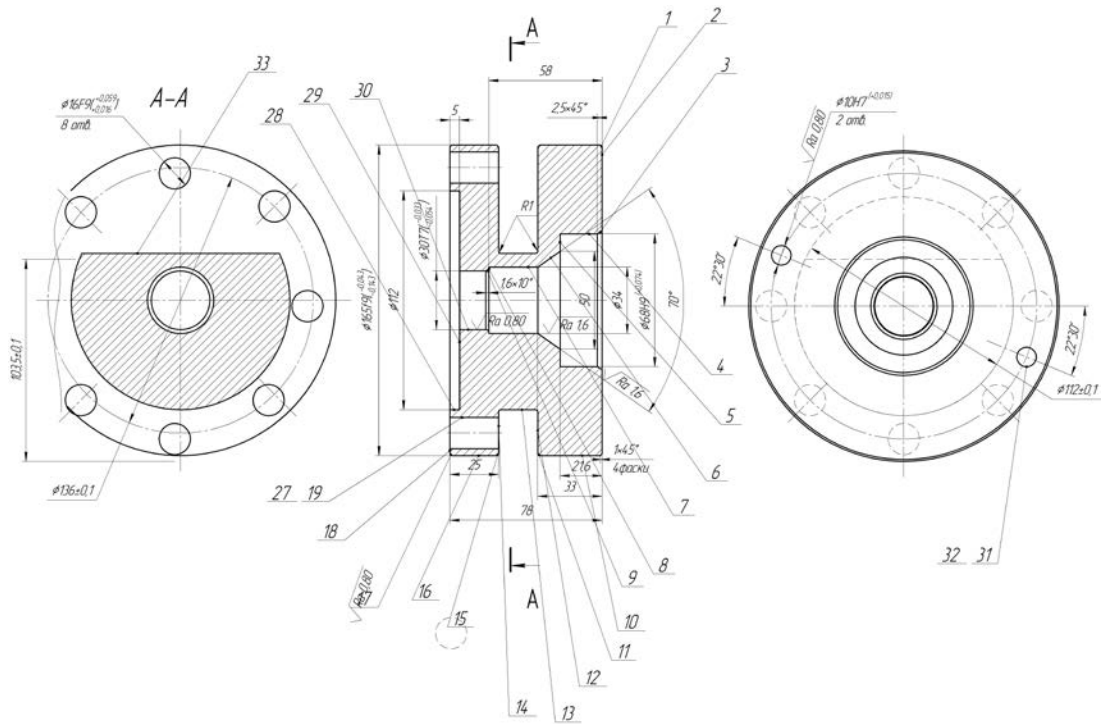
Ескіз деталі Корпус нижній НПО-22.05.01.007 з нумерацією поверхонь
